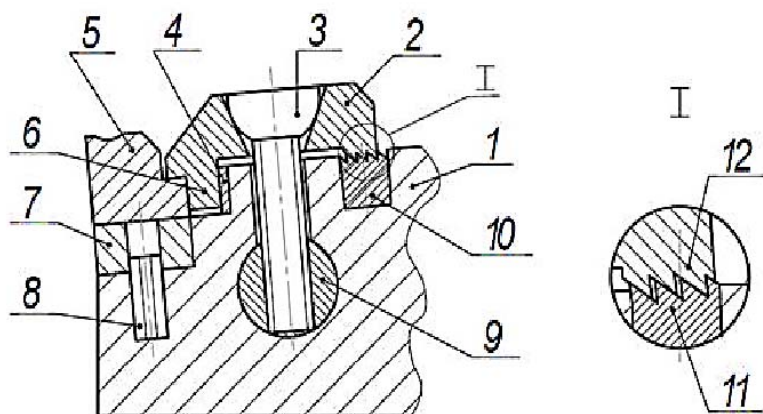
Сборный резец по авторским свидетельствам №1000160 и 1201064 (конструкция 3)
